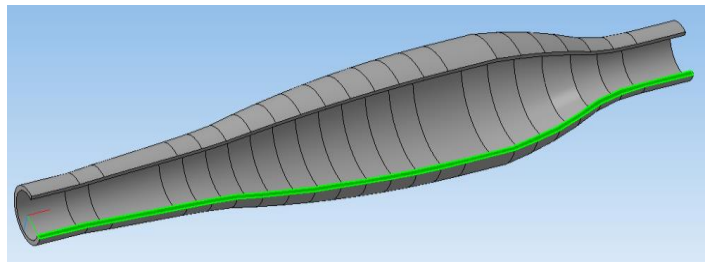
Ескіз розрахованого контуру робочої поверхні резонаторної труби
